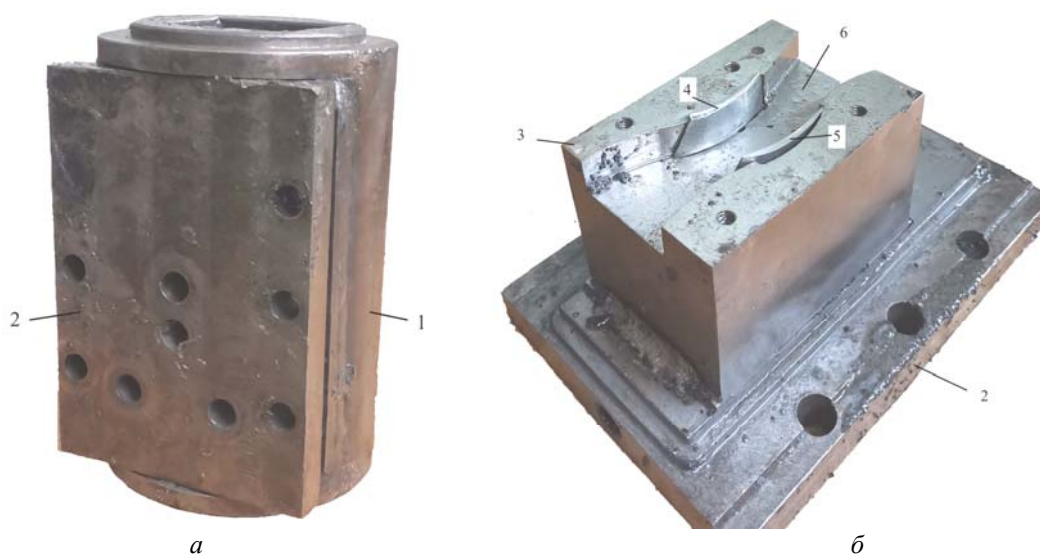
Приспособление – имитатор внутреннего канала литой заготовки:
